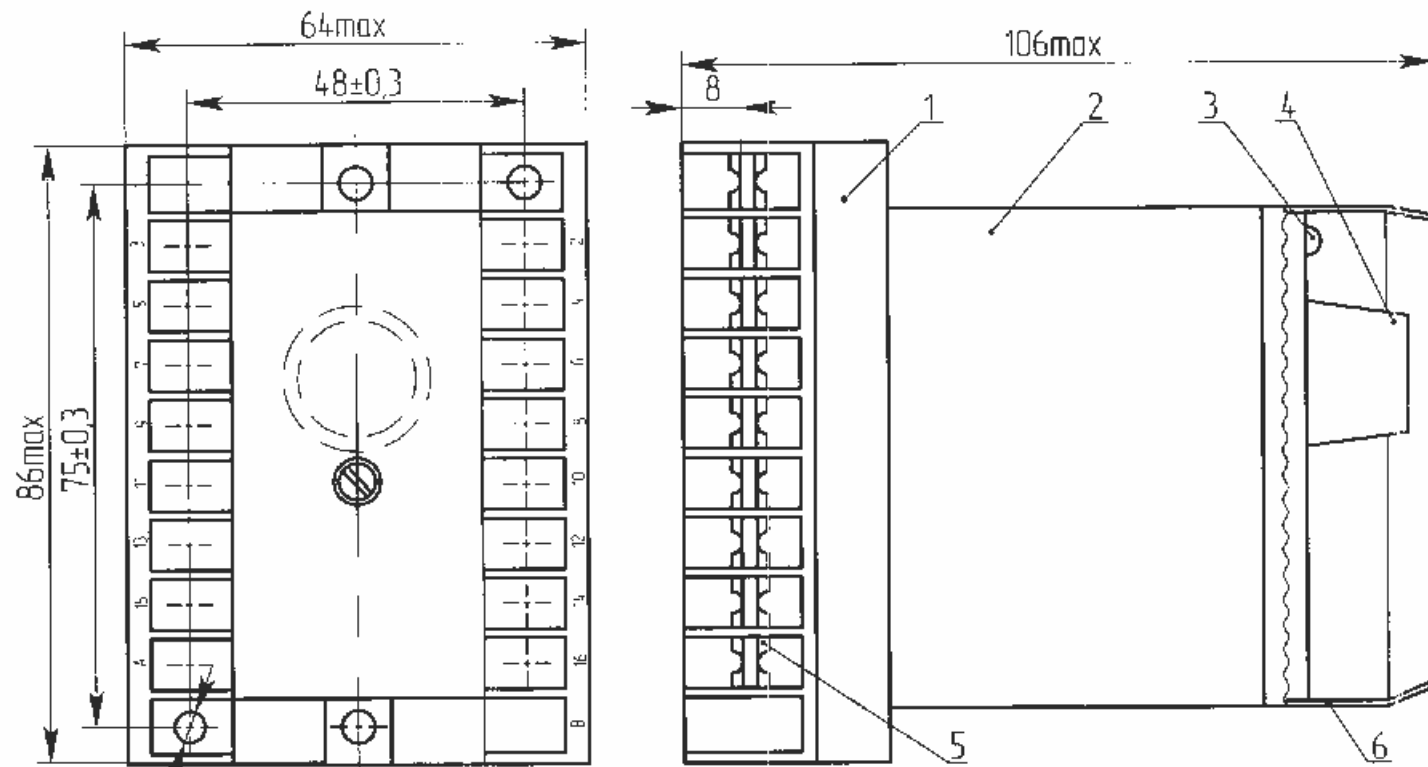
Реле типов PCB18-11-XXXX1, PCB12-XXXX1, PCB18-11-XXXX2, PCB12-XXXX2
